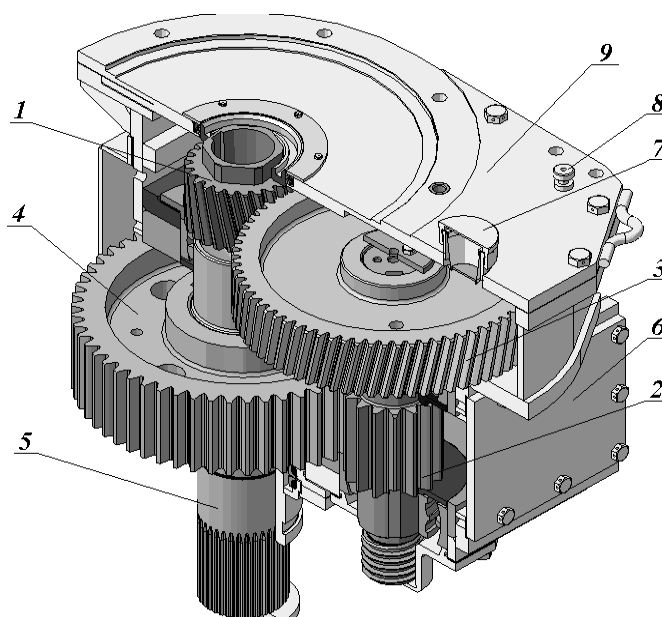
Редуктор вращателя: 1 – ведущая шестерня; 2 – вал-шестерня; 3 – зубчатое колесо; 4 – колесо; 5 – вал; 6 – крышка; 7 – сапун; 8 – шуп; 9 – фланец
